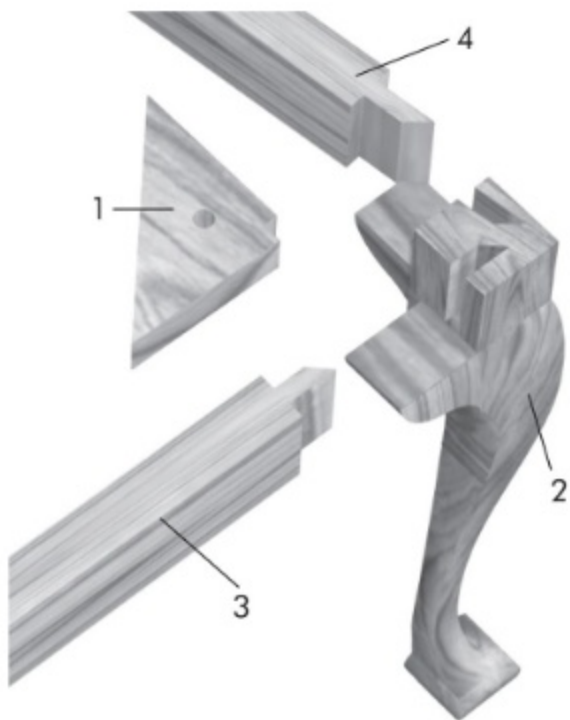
Detalle del ensamble de las traviesas con la pata cabriolé: 1. escuadra de refuerzo; 2. pata delantera; 3. traviesa frontal; 4. traviesa lateral
